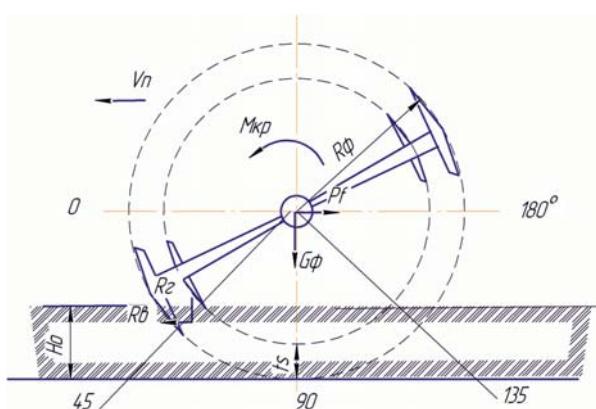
Схема к расчету диаметра фрезерного барабана с двухступенчатыми ножами В-образной формы
